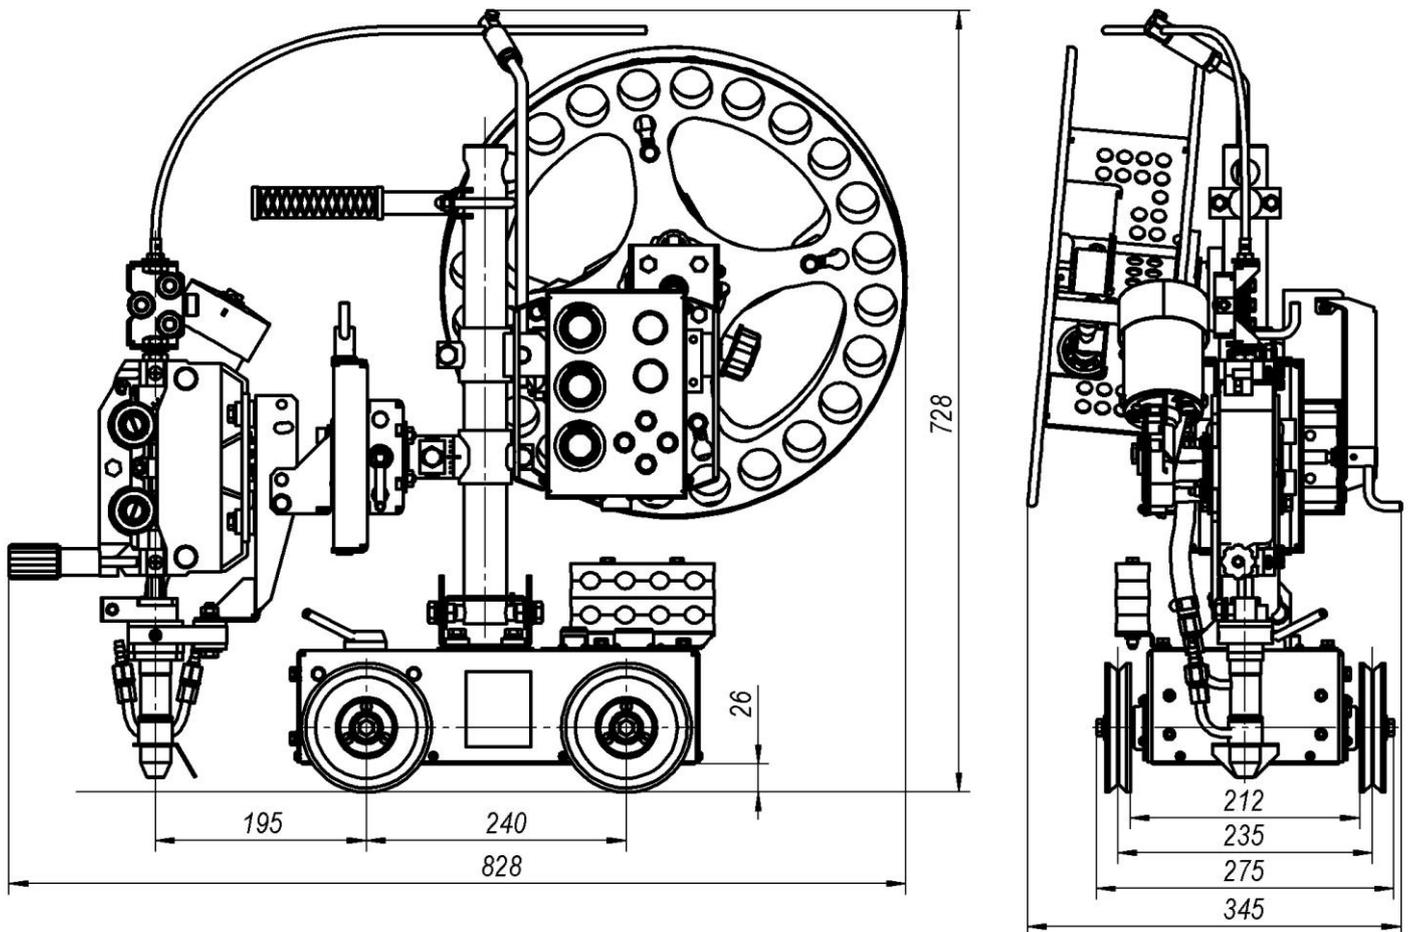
Автомат сварочный АДГ-630 исп.00. Габаритный чертеж.
